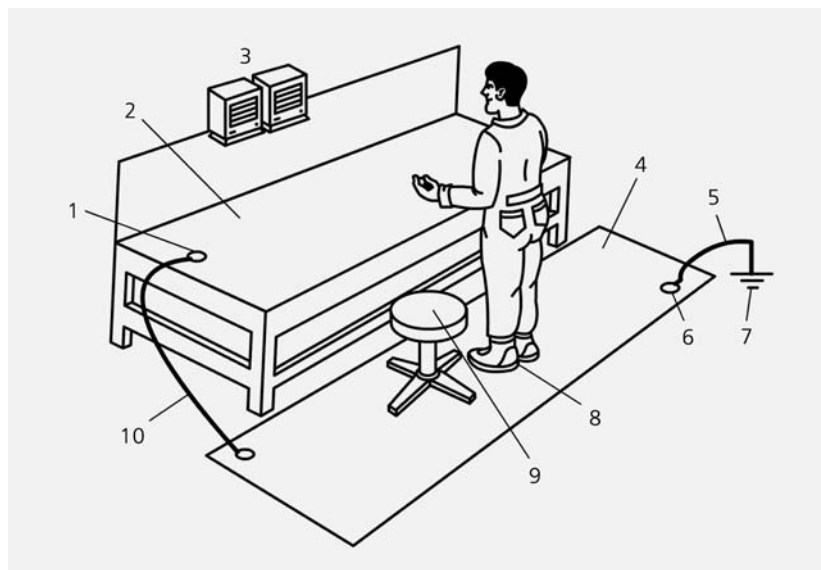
Схема защищенного рабочего места: 1 — клемма заземления; 2 — поверхность стола; 3 — источник ионизированного воздуха; 4 — проводящий коврик; 5 — заземляющий провод; 6 — клемма заземления; 7 — заземление; 8 — проводящая обувь; 9 — проводящая обивка стула; 10 — соединительный провод.
